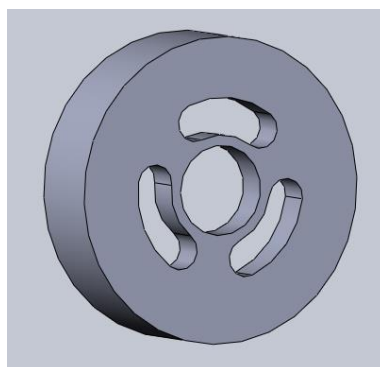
дистанционное кольцо между четвёртой ступенью редуктора и корпусом
